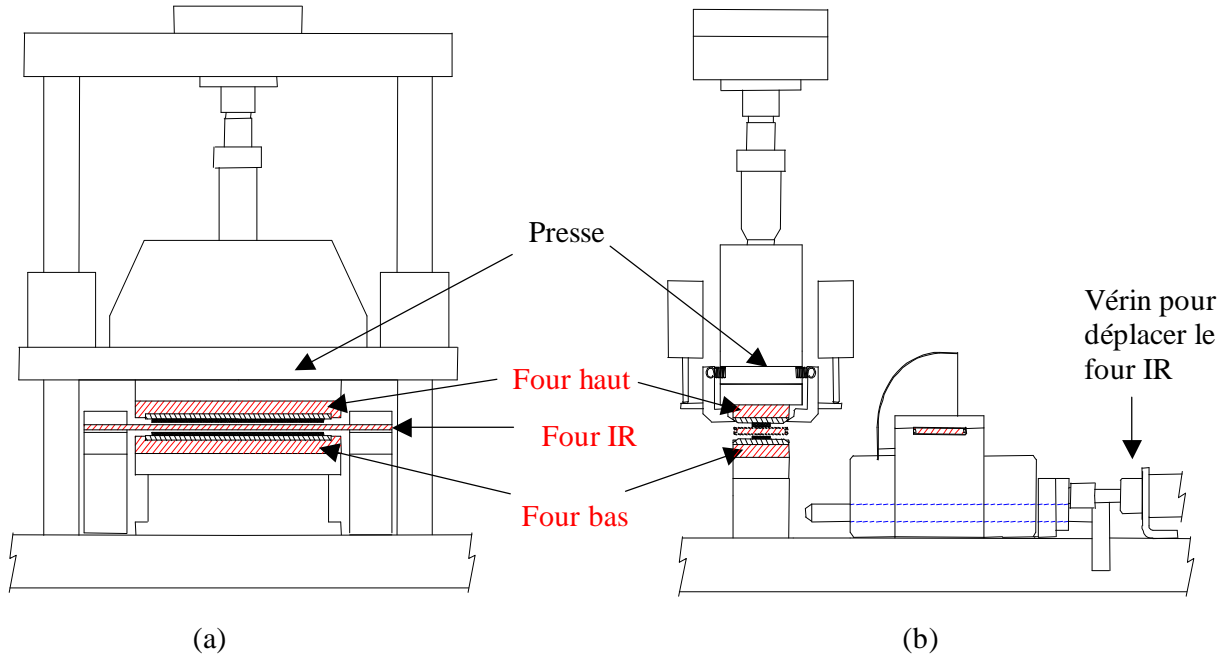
21 : Dessins techniques du dispositif de soudage développé : (a) coupe transverse, (b) coupe longitudinale
